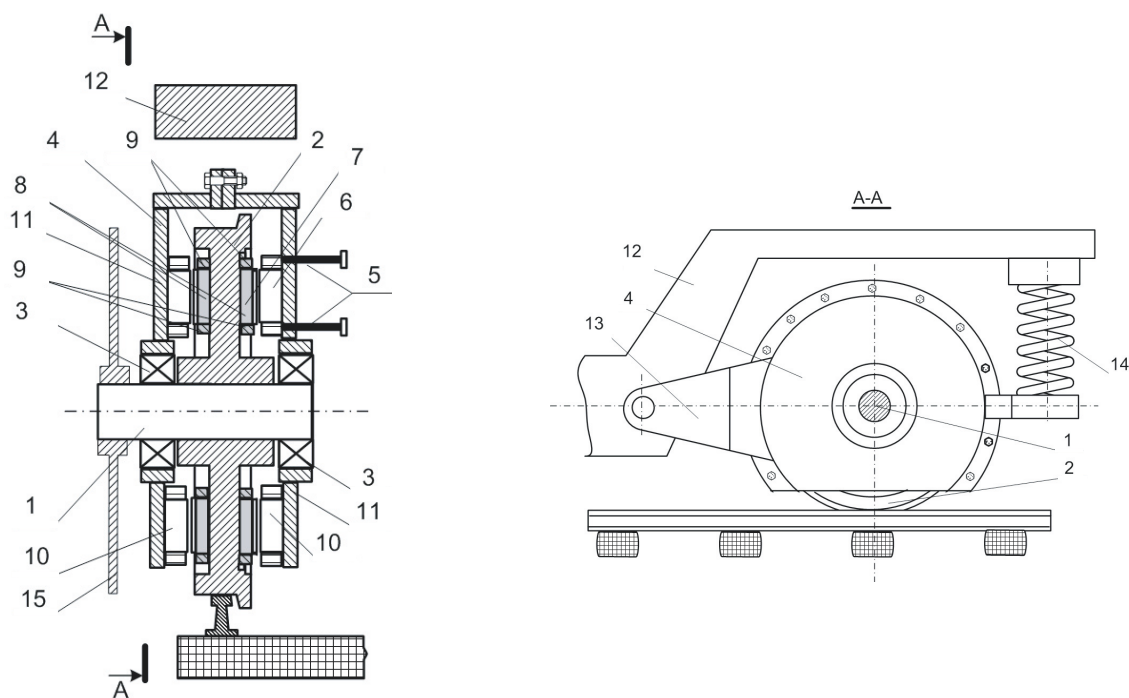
Мотор-колесо с торцовым двигателем и подвижной осью: 1 – ось; 2 – колесо; 3 – подшипниковый узел; 4 – торцевой асинхронный двигатель; 5 – система охлаждения; 6 – статор; 7 – обмотка ротора; 8 – проводники обмотки; 9 – короткозамыкающие кольца; 10 – кольцеобразные активные части статора; 11 – полупроводники; 12 – рама тележки; 13 – поводок; 14 – упругий элемент; 15 – тормозной диск
